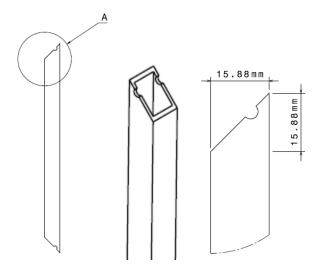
Exemplo de como devem ser cortados os tubos de alumínio de 430 mm e 215 mm.
